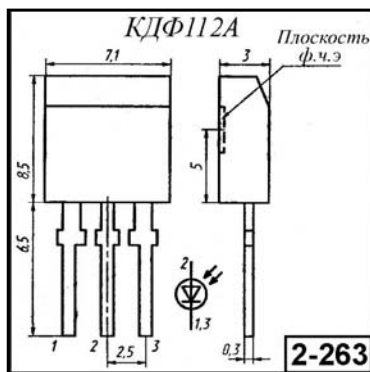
Внешний вид, габаритные размеры кремниевых фотодиодов
